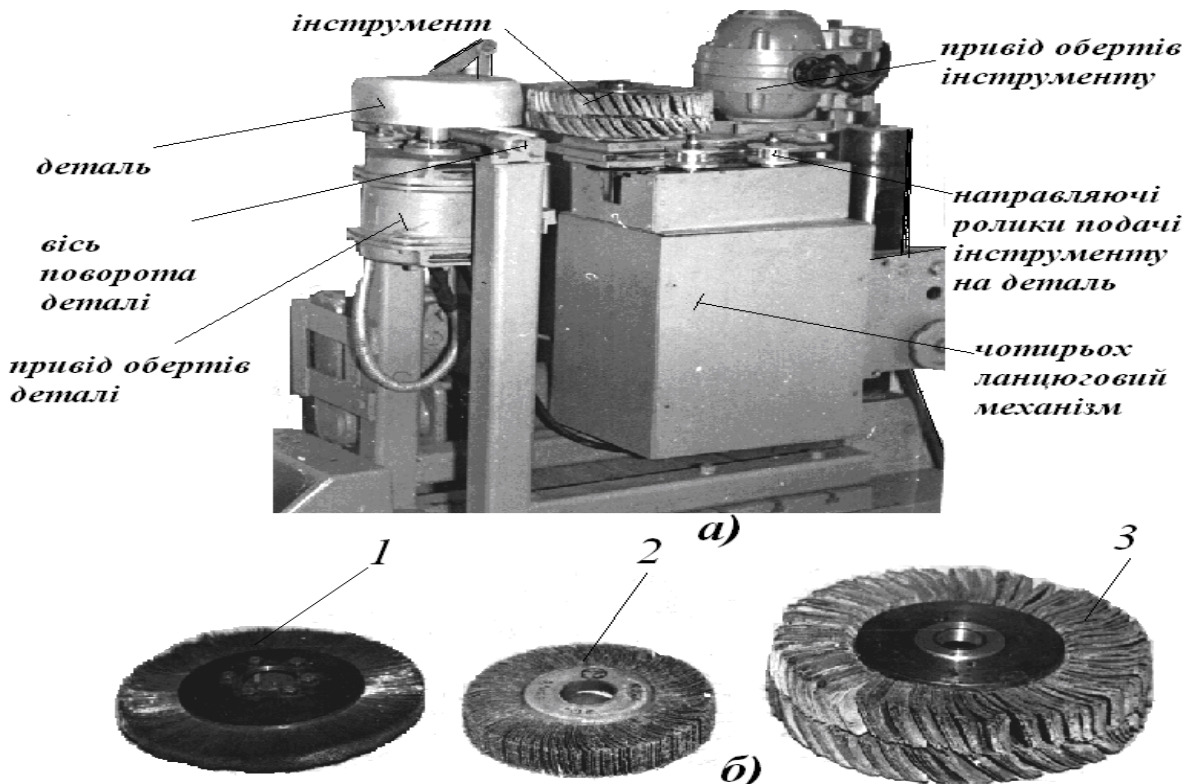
Обладнання для абразивної обробки зовнішньої поверхні деталей термосу (а) й абразивний та лезовий інструмент (б)
